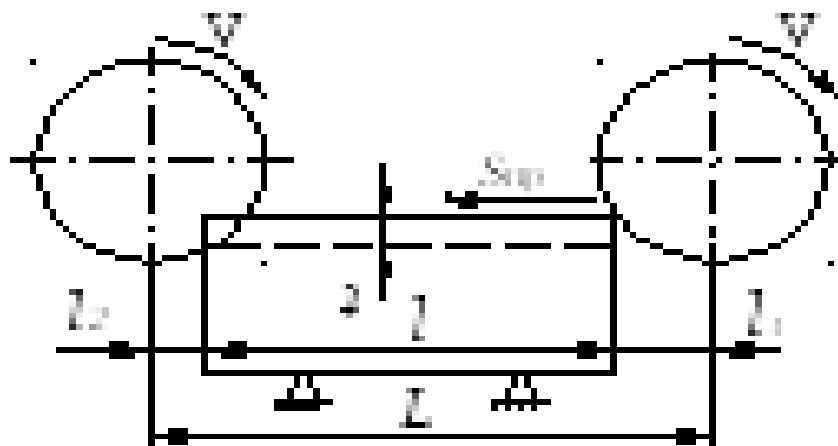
Схема обработки цилиндрической фрезой
